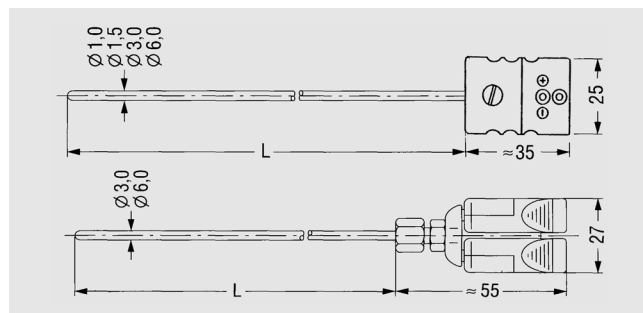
/87 Термопара с соединительной розеткой; сверху с одним сенсором, снизу с двумя сенсорами; размеры
